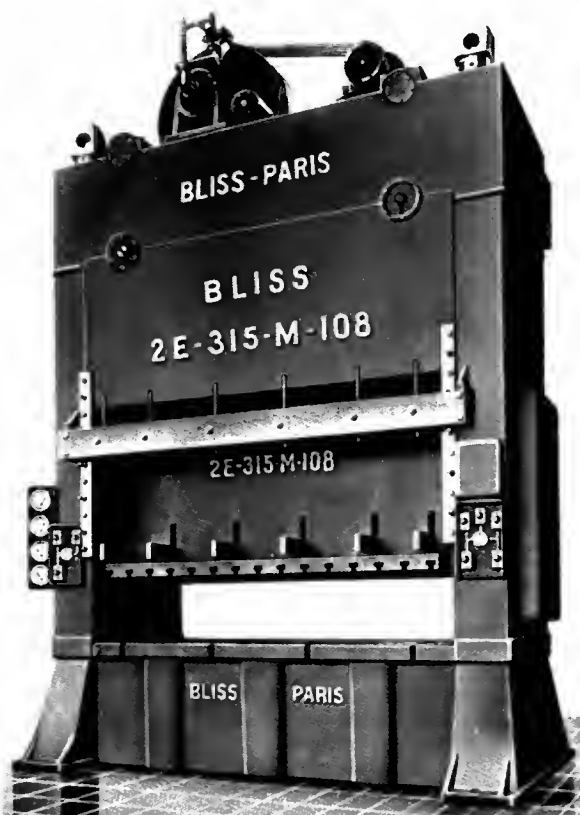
Presse à simple action du type assemblé à arbres transversaux pour carrosserie automobile (E. W. Bliss)
